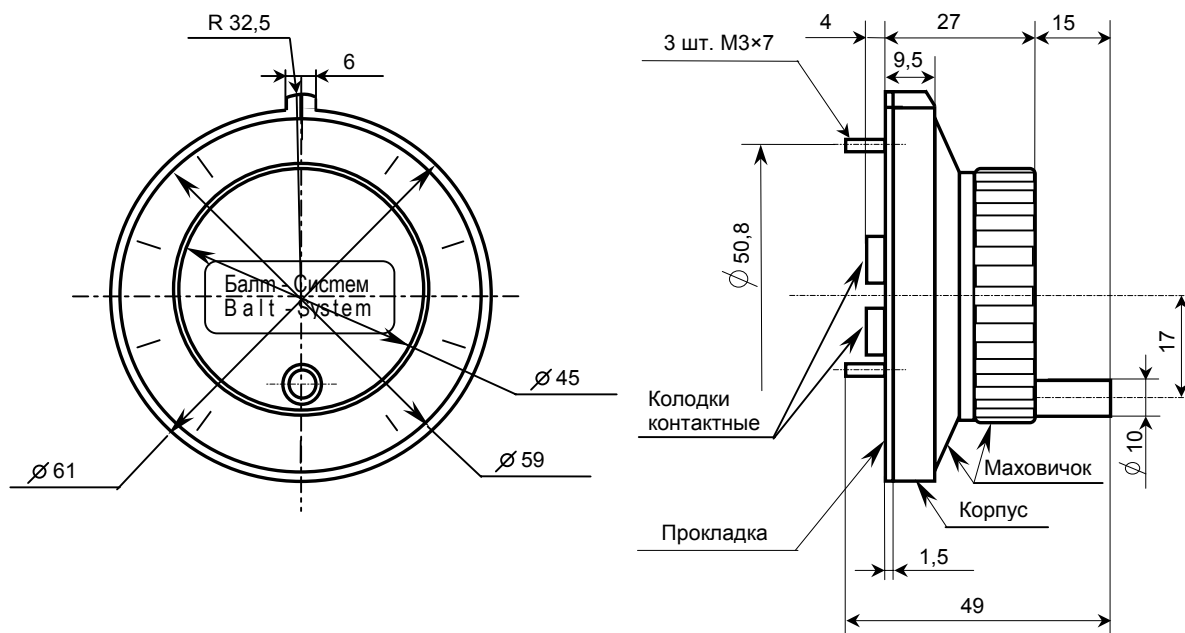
Габаритные размеры штурвала ZBG-5-003-100
